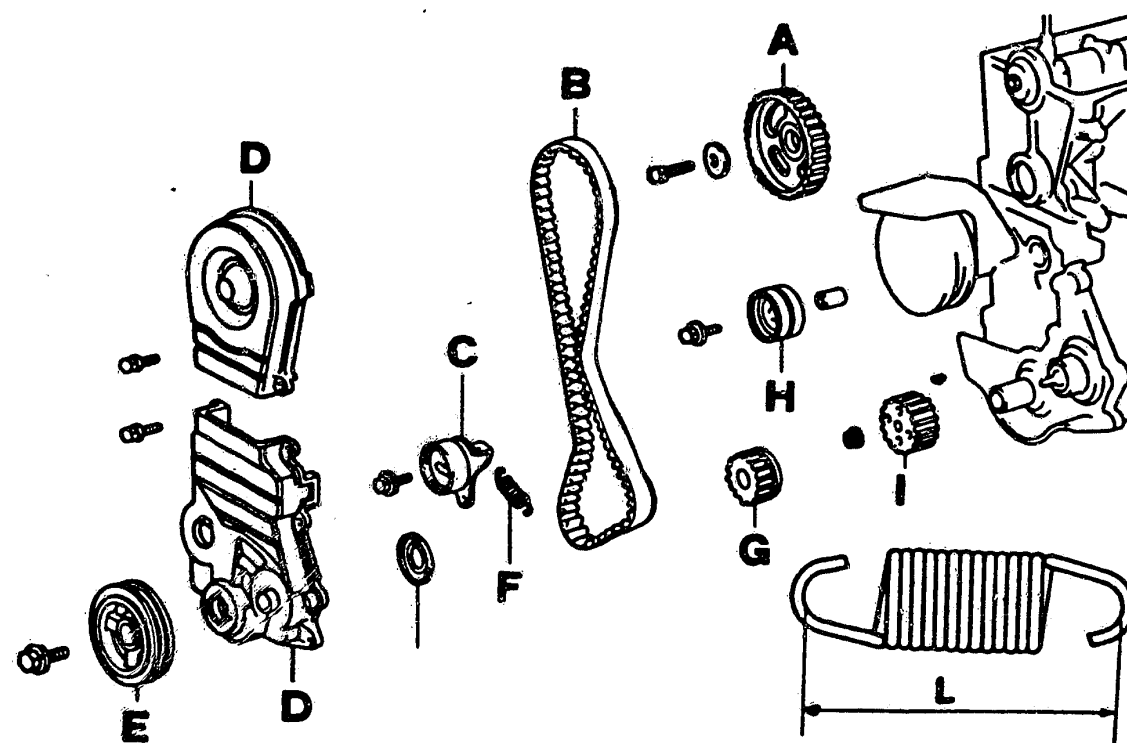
Einzelteile der Motorsteuerung: Die freie Länge L der Spannfeder F beträgt 38,4 mm. Bei einer Zugkraft von 50N muss die Länge 51,5mm betragen. A Nockenwellenrad – B Zahnriemen – D Kunststoffabdeckungen – E Kurbelwellen-Riemenscheibe – F Spannfeder – G Kurbelwellenrad – H Umlenkrad – I Ölpumpenantriebsrad.
